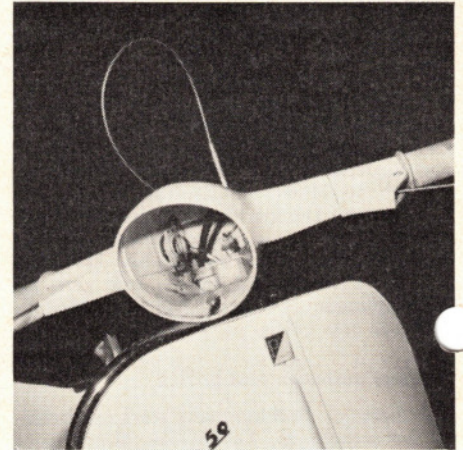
Soll ein neues Bowdenseil für einen der Handhebel eingezogen werden, so wird es vorteilhaft so eingefädelt, wie hier gezeigt; Hülle zurückgezogen und durch die Tachoöffnung im Lenker nach oben gesteckt, dort wird das im Bogen geführte Seil eingeführt.
